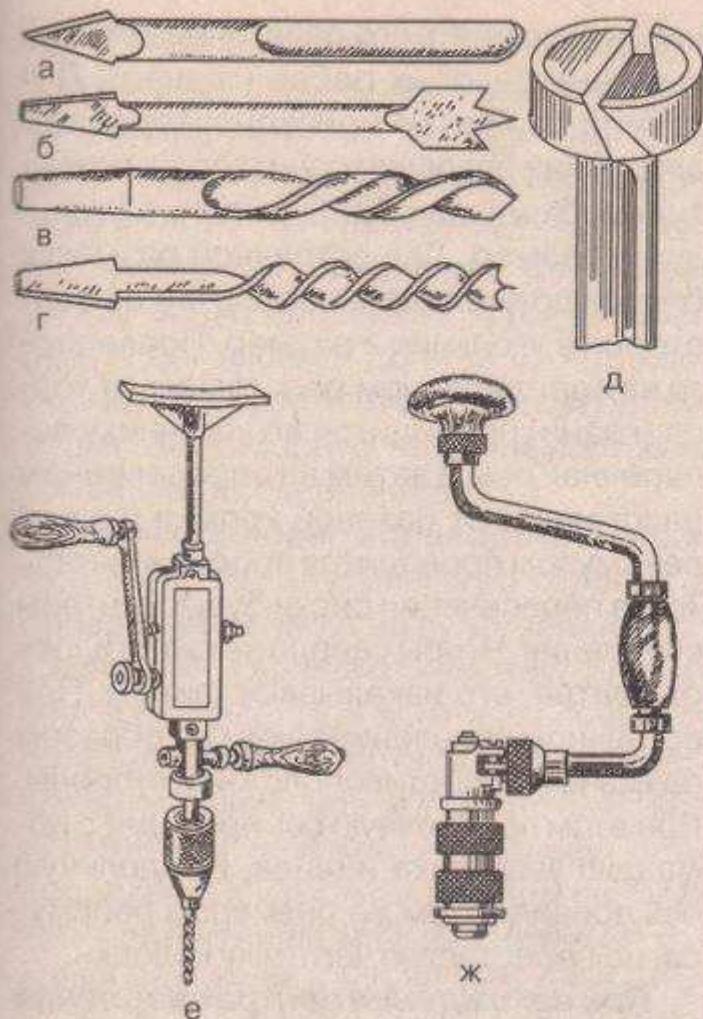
Сверла и инструменты для работы с древесиной: а — первое; б — центральное; в — спиральное; г — винтовое; д — сверло с круговым подрезателем; е — ручная дрель; ж — коловорот
